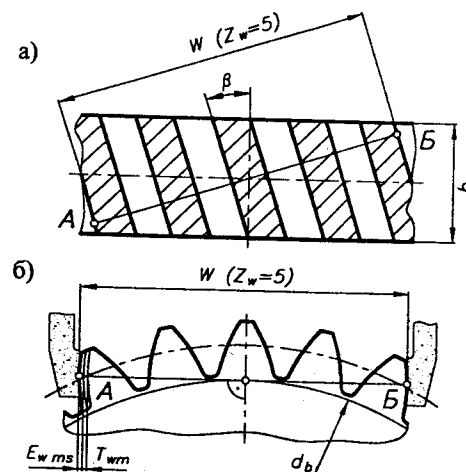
Схема замера длины общей нормали W при числе охватываемых зубьев $Z_w = 5$ для цилиндрических колес: а) косозубых; б) прямозубых, а также расположение отклонений и допусков
